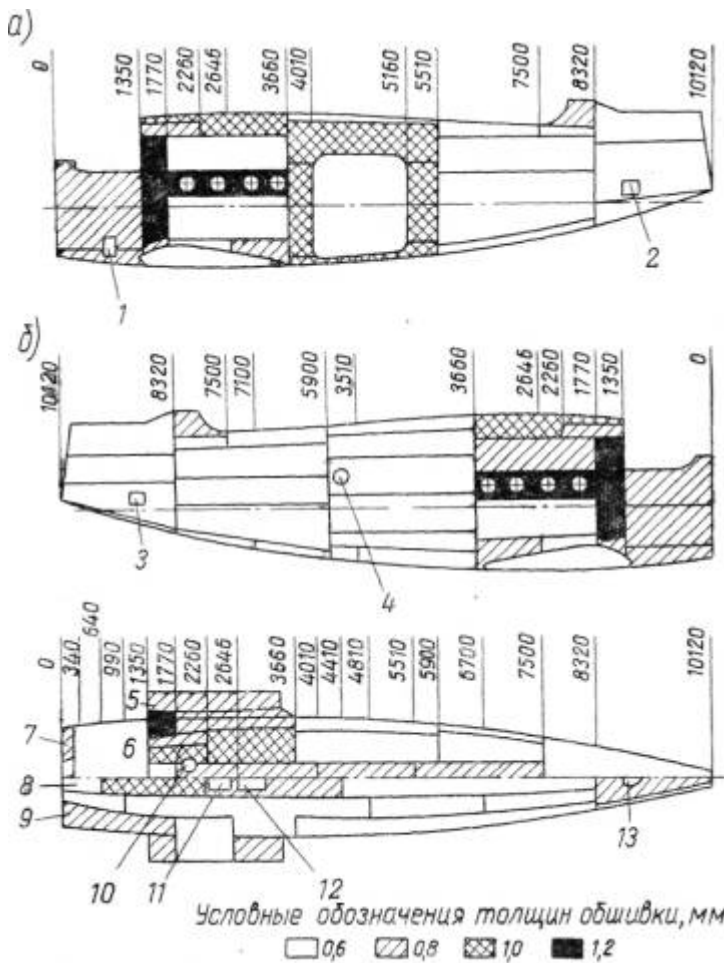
Схема обшивки фюзеляжа: а — вид на левый борт; б — вид на правый борт;
